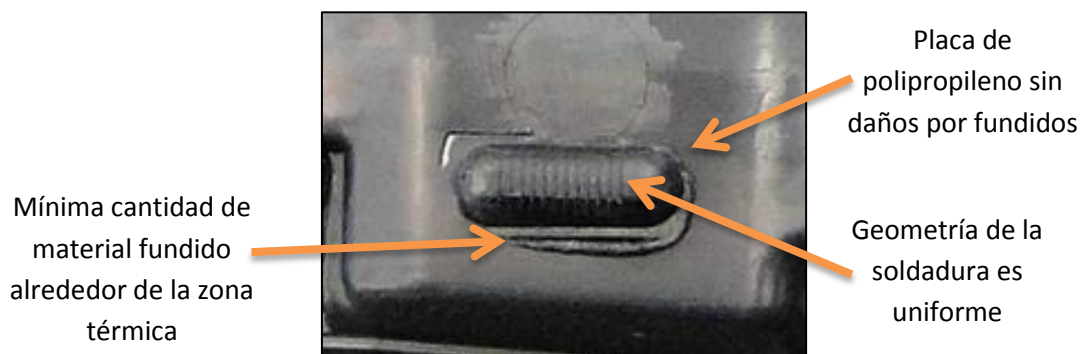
Soldadura lineal con mayor fuerza de desprendimiento.
